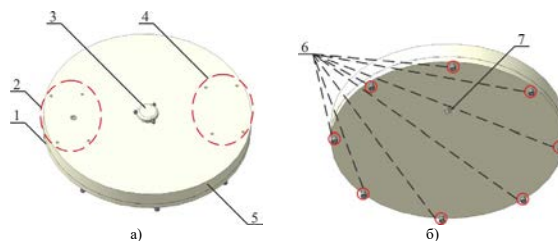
Зовнішня 3D модель поворотної платформи а) – вид збоку кришки; б) – вид збоку корпусу; 1) – корпус; 2) – місце установки МК № 2; 3) – фланець; 4) – місце установки МК № 1; 5) – кришка; 6) – місця кріплення платформи до ПА; 7) – пробка
